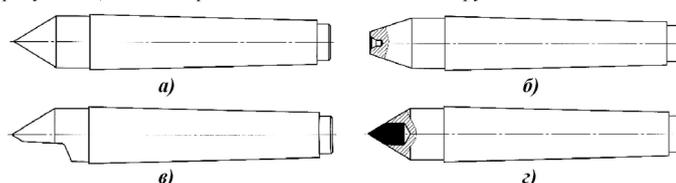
Типы невращающихся задних центров: а) жесткий центр; б) обратный центр; в) полуцентр; г) твердосплавный центр
